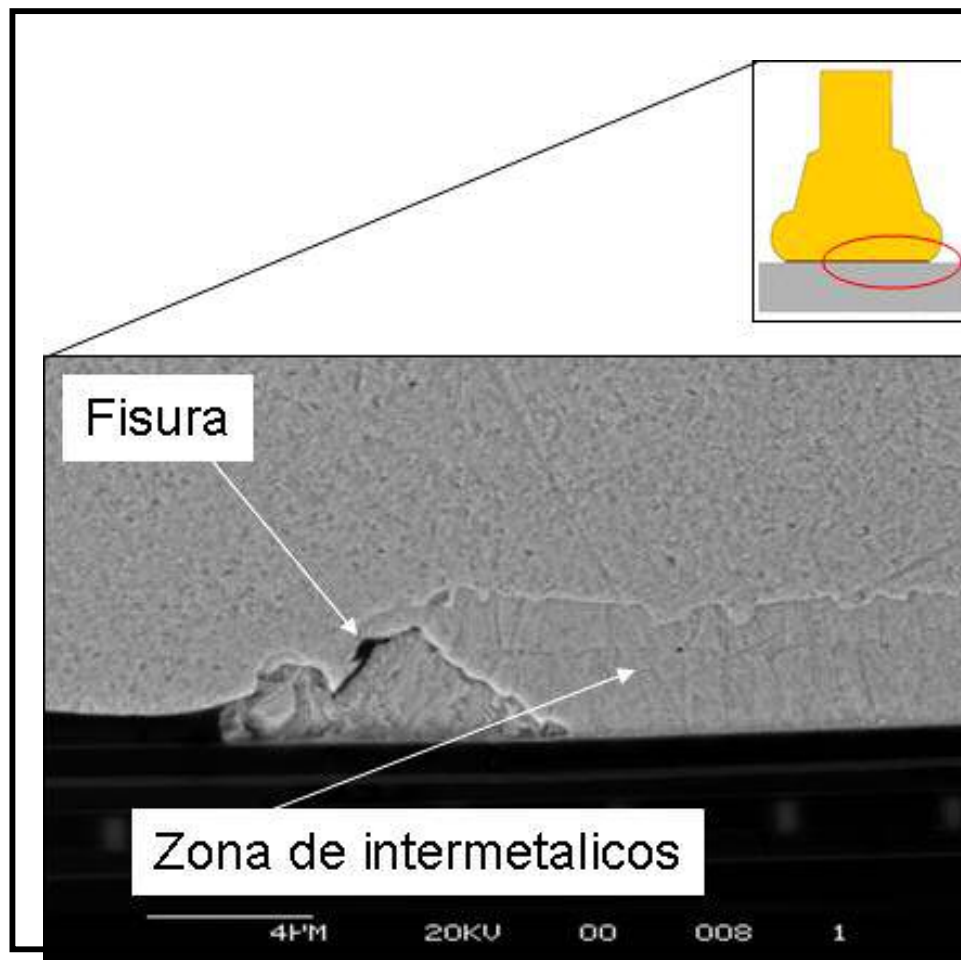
Acercamiento a esquina inferior izquierda de fig 3.12.
